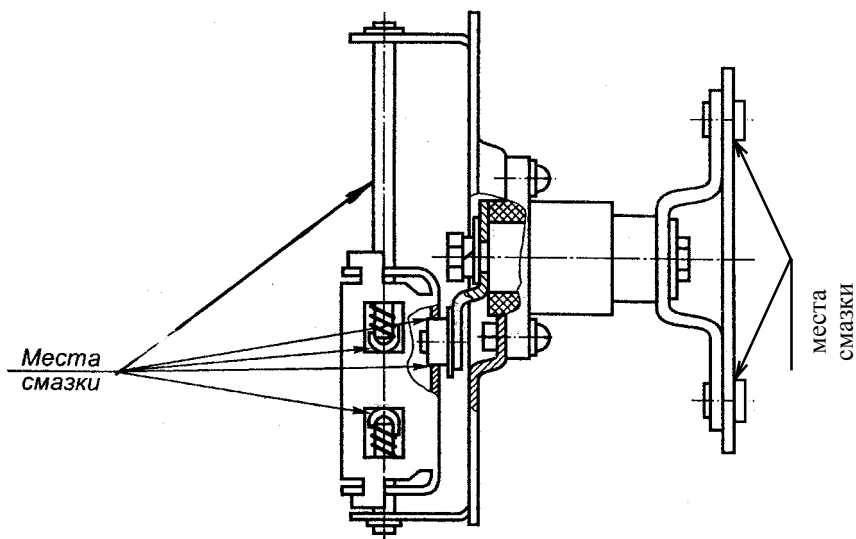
Места смазки ручного дистанционного привода выключателей выдвижного исполнения.
